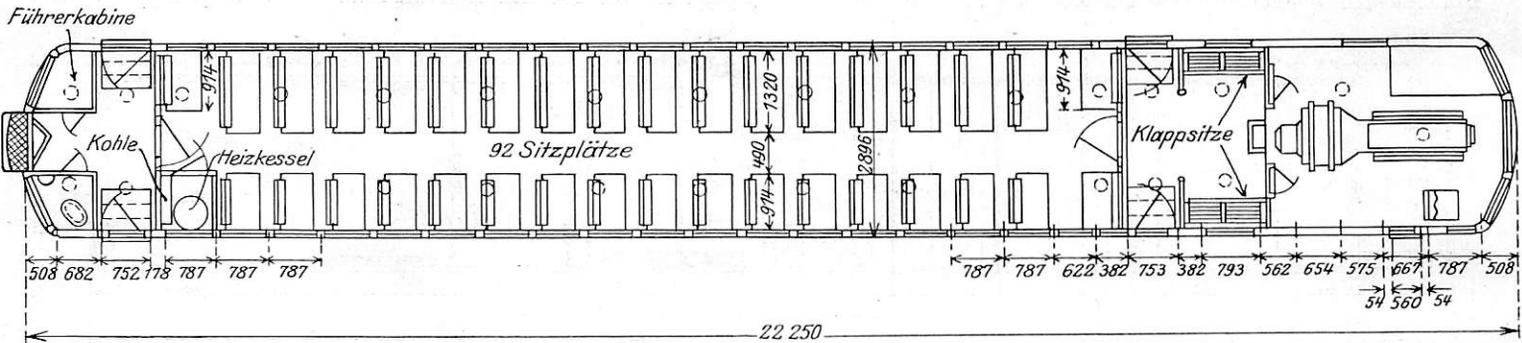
Grundriß des 250 PS Triebwagens Brill. 73 Fuß-Wagen.
